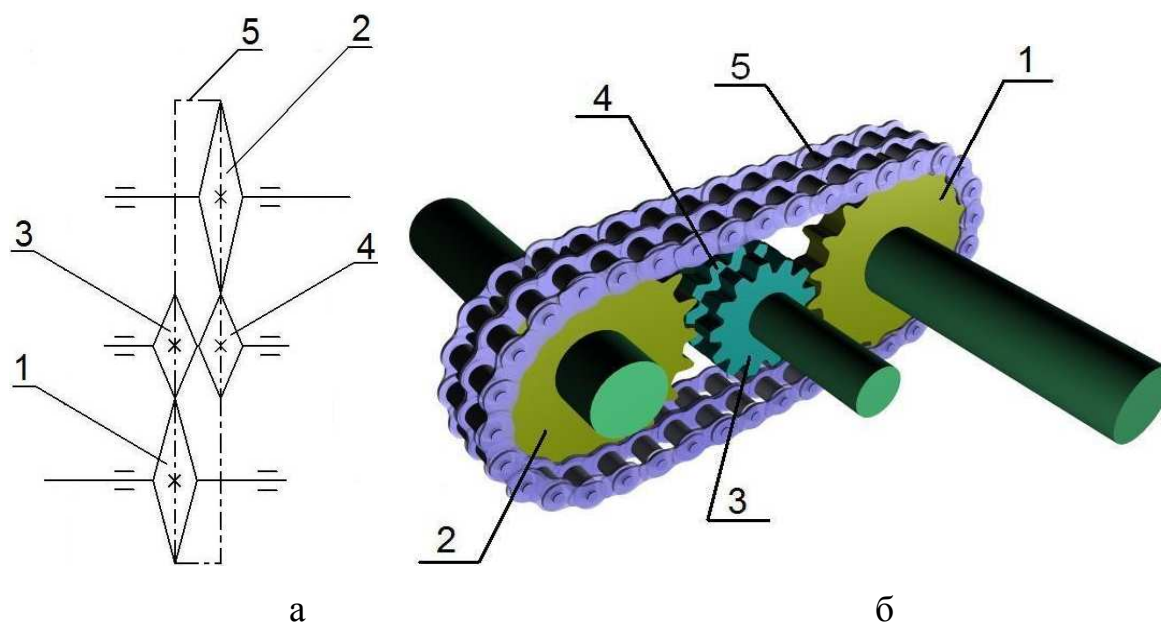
Зубчато-цепная передача с двухрядной цепью:
